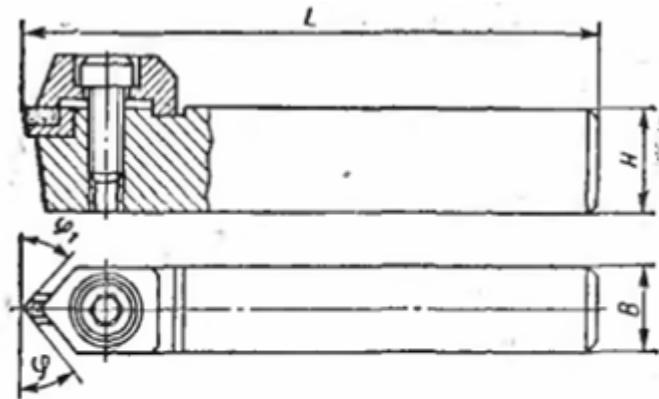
Резец сборный проходной с механическим креплением режущей вставки
